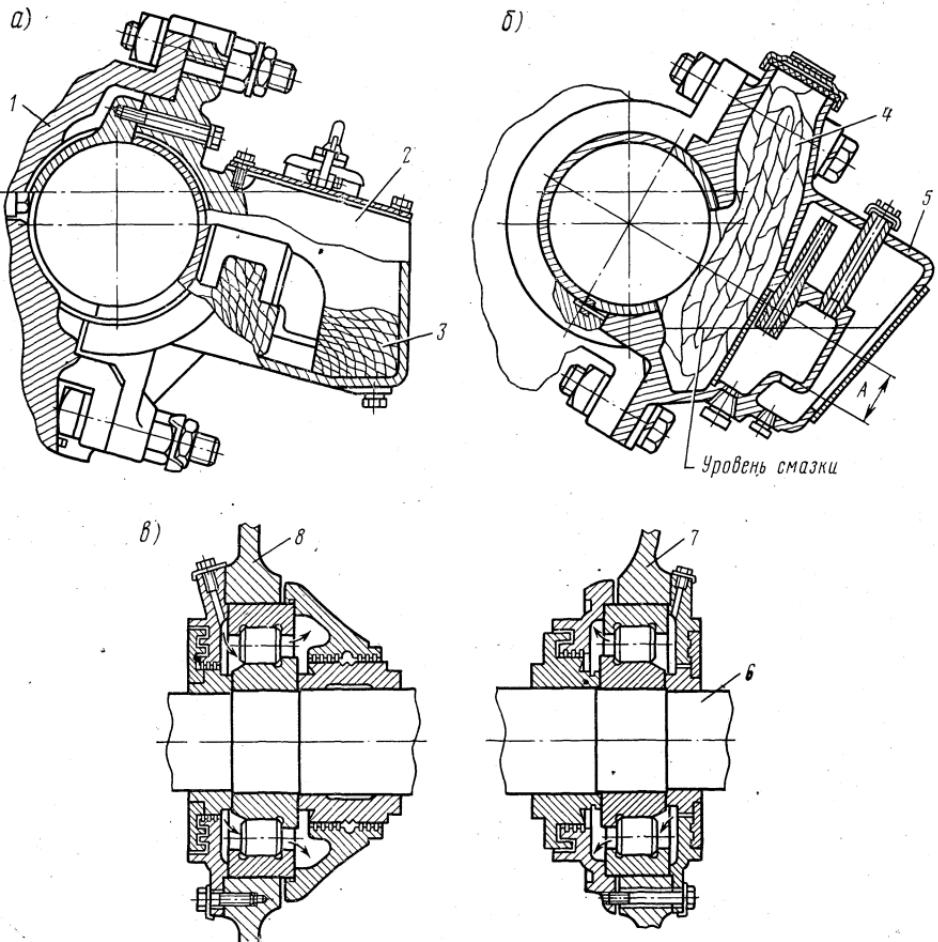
Буksы моторно-подшипниковые с польстером (а), постоянным уровнем смазки (б) и подшипниковые щиты (в) тягового двигателя НВ-406Б (стрелками указаны места добавления смазки):
